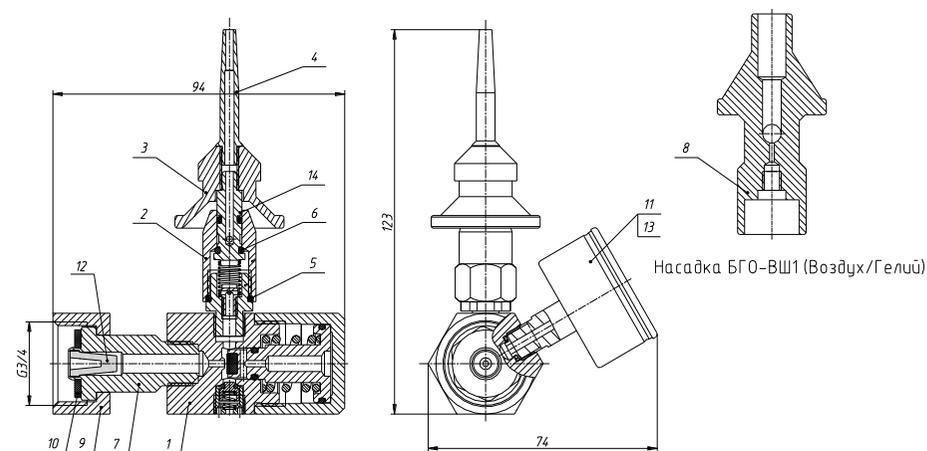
Редуктор баллонный гелиевый одноступенчатый типа БГО-ВШ1.
